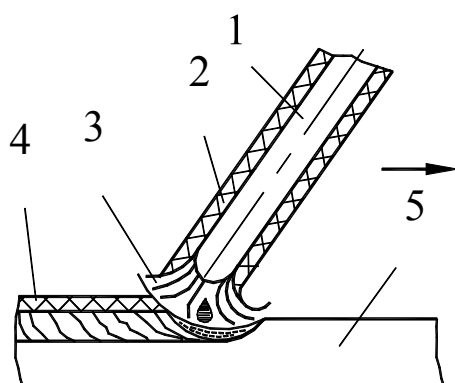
Схема процесса ручной дуговой сварки [58]: 1 – электрод, 2 – покрытие электрода, 3 – защитный газ, 4 – шлак, 5 – изделие
